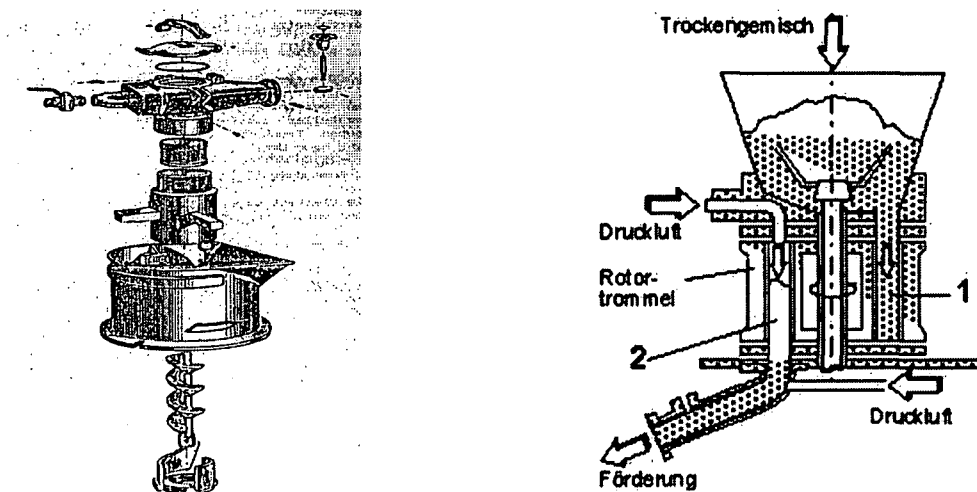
Schneckenmaschine (linkes Bild) und Rotormaschine (rechtes Bild) - [30]
